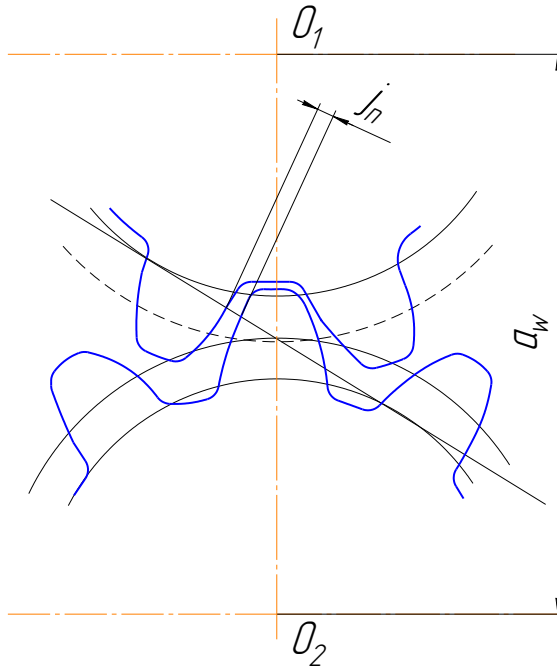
Схема образования бокового зазора в зацеплении зубчатых колес
